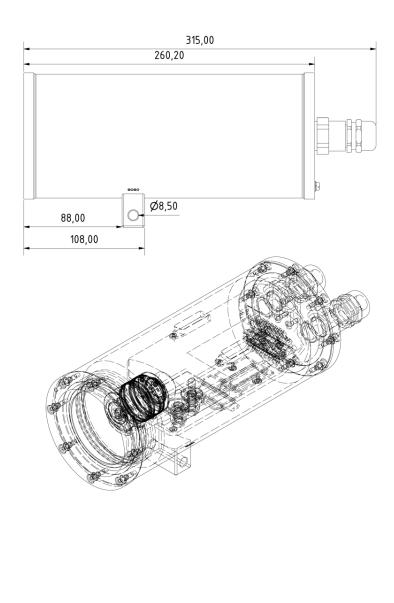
Abmessungen T08 ExCam IP135x mit K1 Flansch
